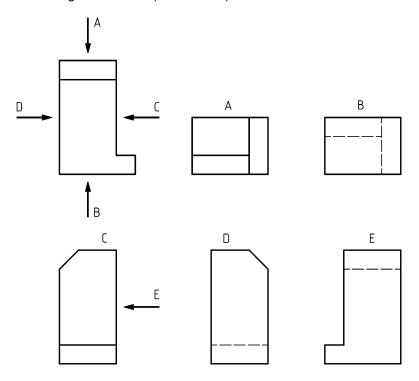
Kennzeichnung der zugehörigen Ansichten
